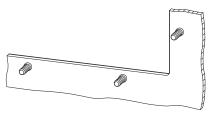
Schweiß-Gewindebolzen M4 x 12 am Blech
